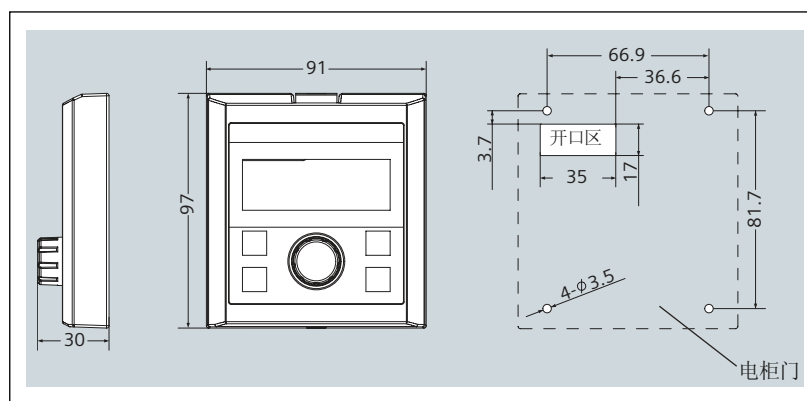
安装尺寸（外形尺寸+钻孔样式+开口尺寸；单位：mm）
